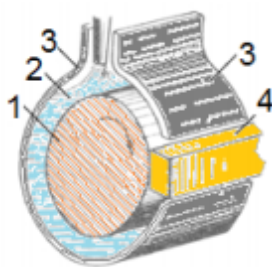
Схема чистої анодно-механічної обробки неметалевим інструментом: 1 – виріб; 2 – електроліт; 3 – катодні пластини; 4 – інструмент для зняття плівки
